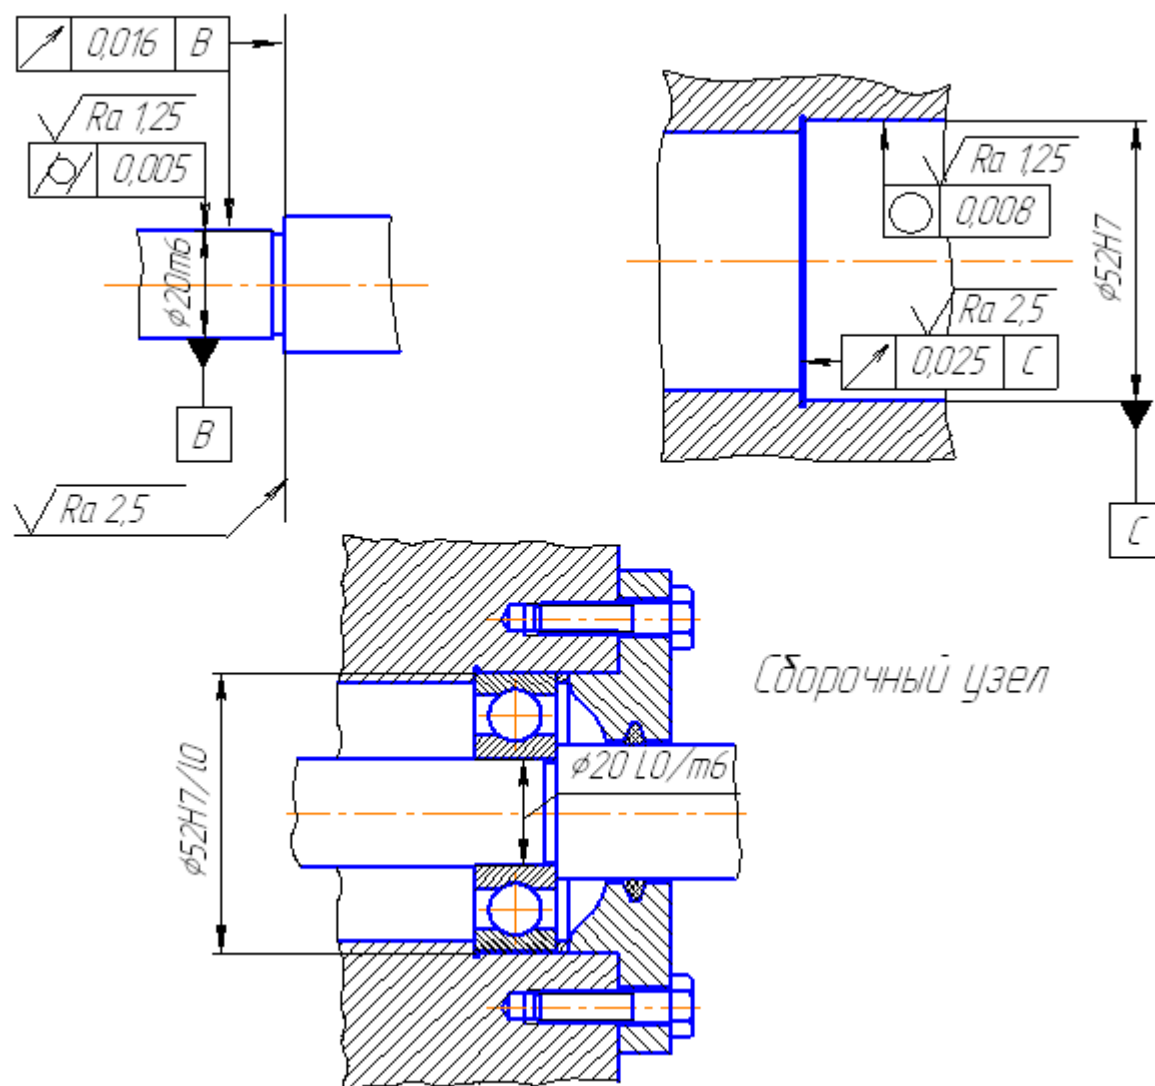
Эскизы сопрягаемых деталей и сборочного узла ПК
